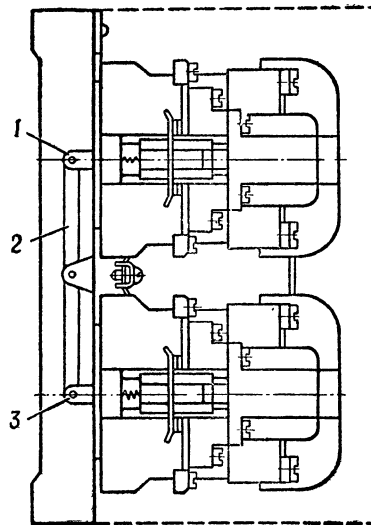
Механическая блокировка реверсивного пускателя.
